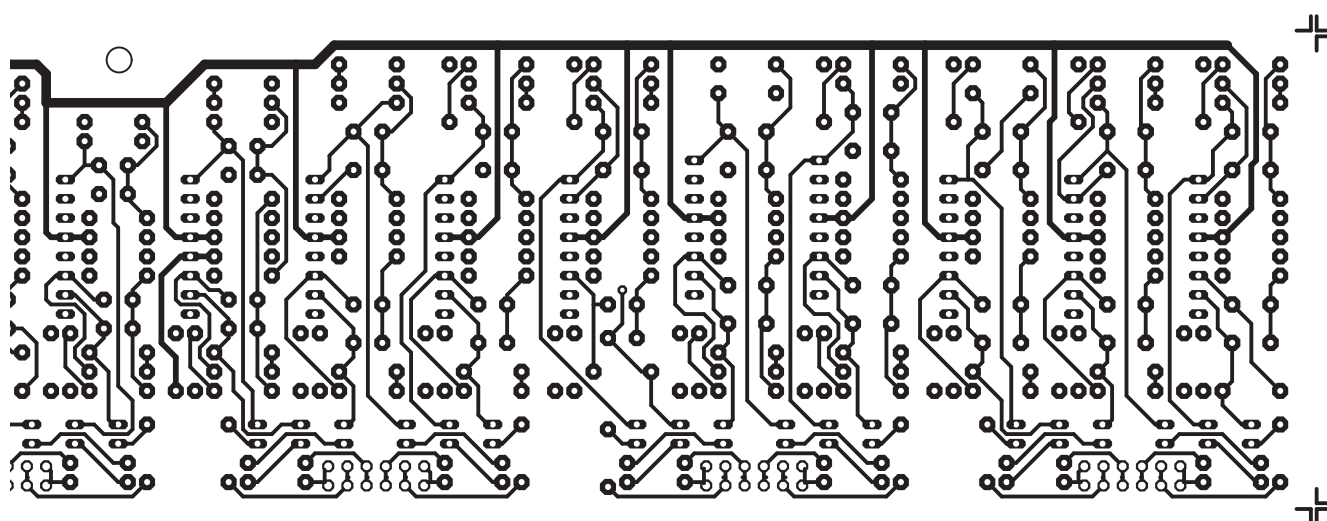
Obrazec desky s plošnými spoji filtrů, strana spojů (BOTTOM)
